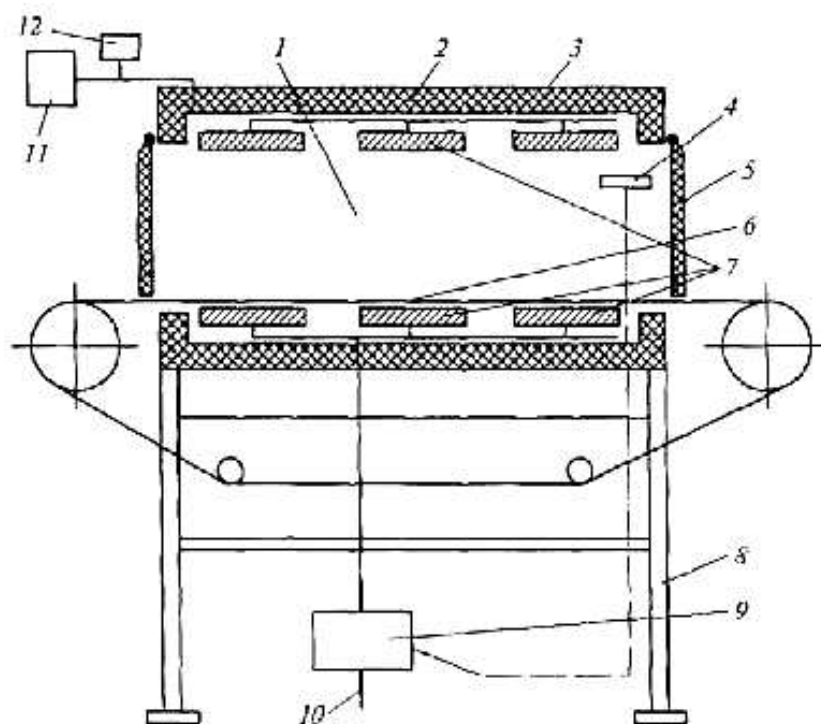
Принципова схема умовного теплового апарату: 1 – робоча камера; 2 – теплова ізоляція; 3 – кожух; 4 – датчики; 5 – дверцята; 6 – транспортер; 7 – нагрівальні елементи; 8 – опорно-несучий елемент конструкції; 9 – блок управління; 10 – система підведення енергії; 11 – система контролю; 12 – система безпеки
